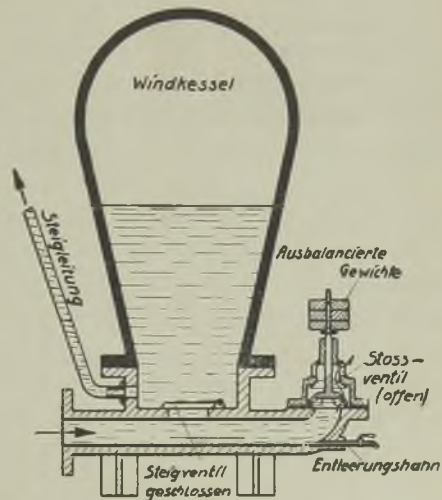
Schnitzzeichnung: Hydraulischer Widder.
